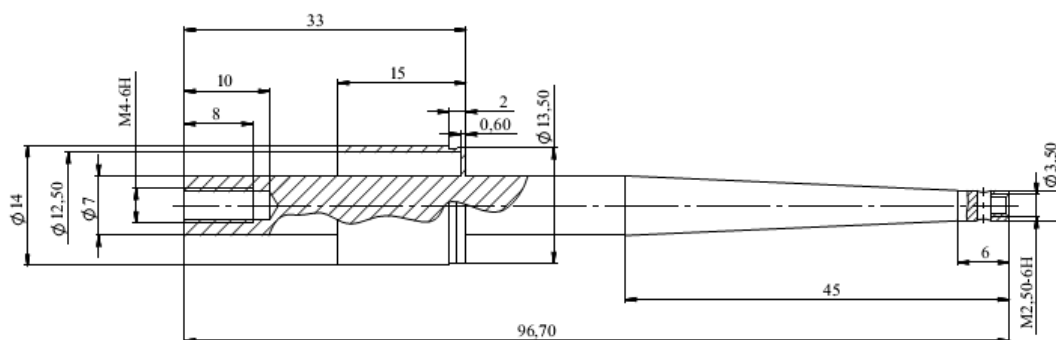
Схема конструкции составного концентратора для ультразвуковой сварки
